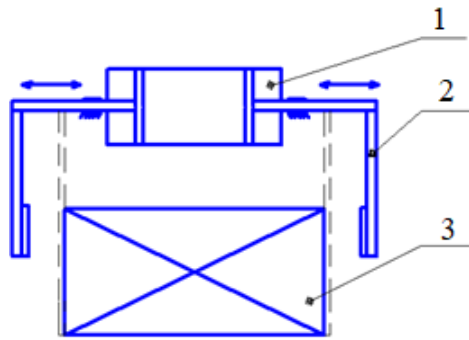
Схема захоплювального пристрою зі зворотно-поступальним рухом стулок: 1- пневмоциліндр двосторонньої дії; 2 - стулки; 3 - упаковка
